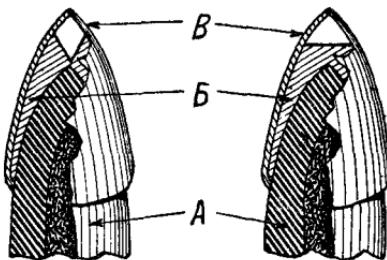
Схемы устройства головной части бронебойного снаряда: А — корпус, Б — бронебойный наконечник, В — баллистический наконечник.
